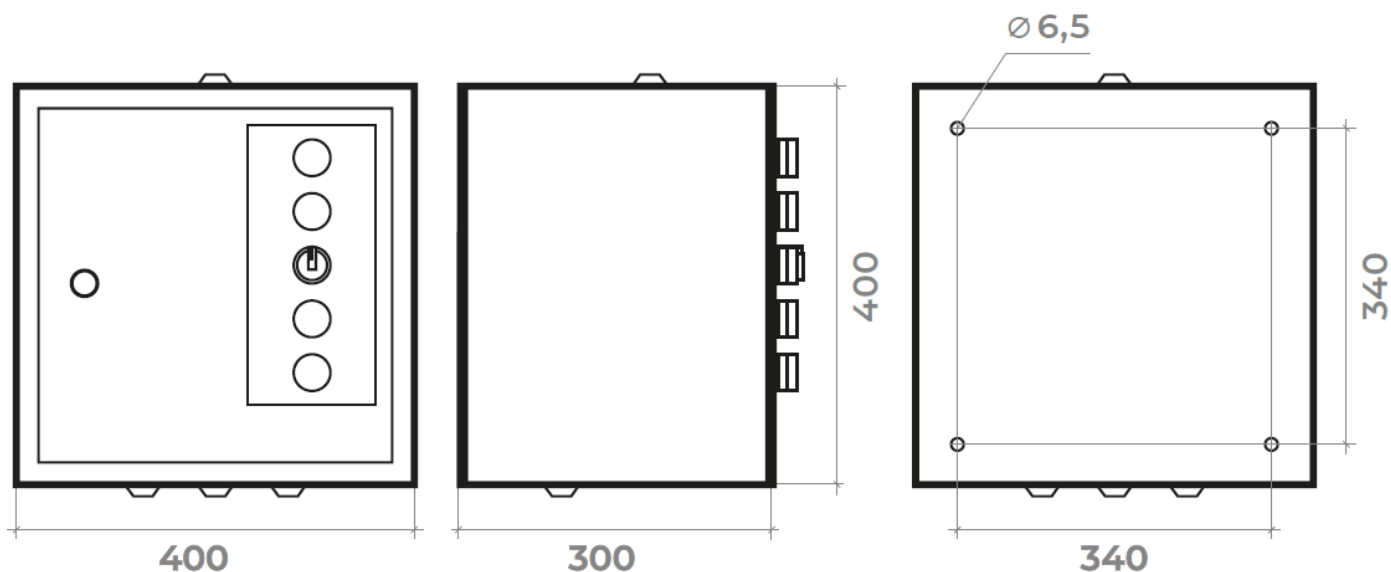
Габаритные и установочные размеры КУПОЛ ШУВ-3К.
